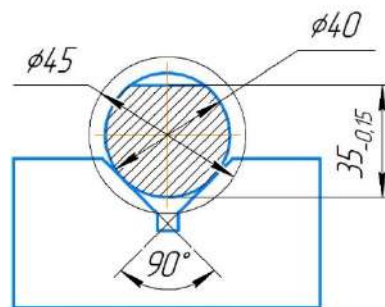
Схема встановлення деталі для фрезерної операції
